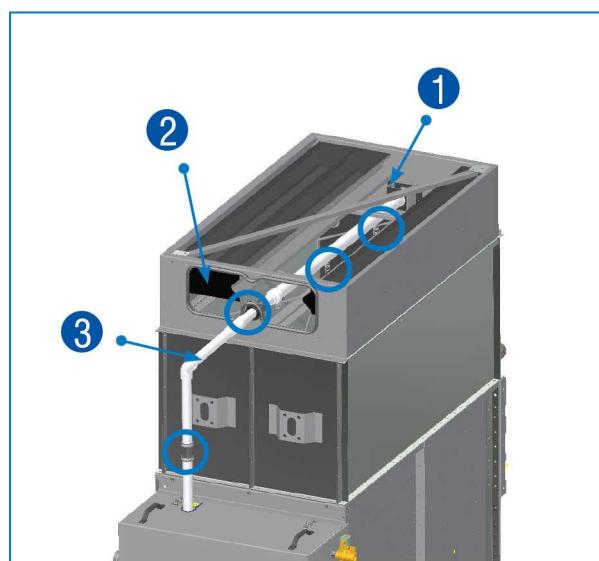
1. Установка оросительной трубы, 2. Установка улавливателя, 3. Установка верхней трубы.
